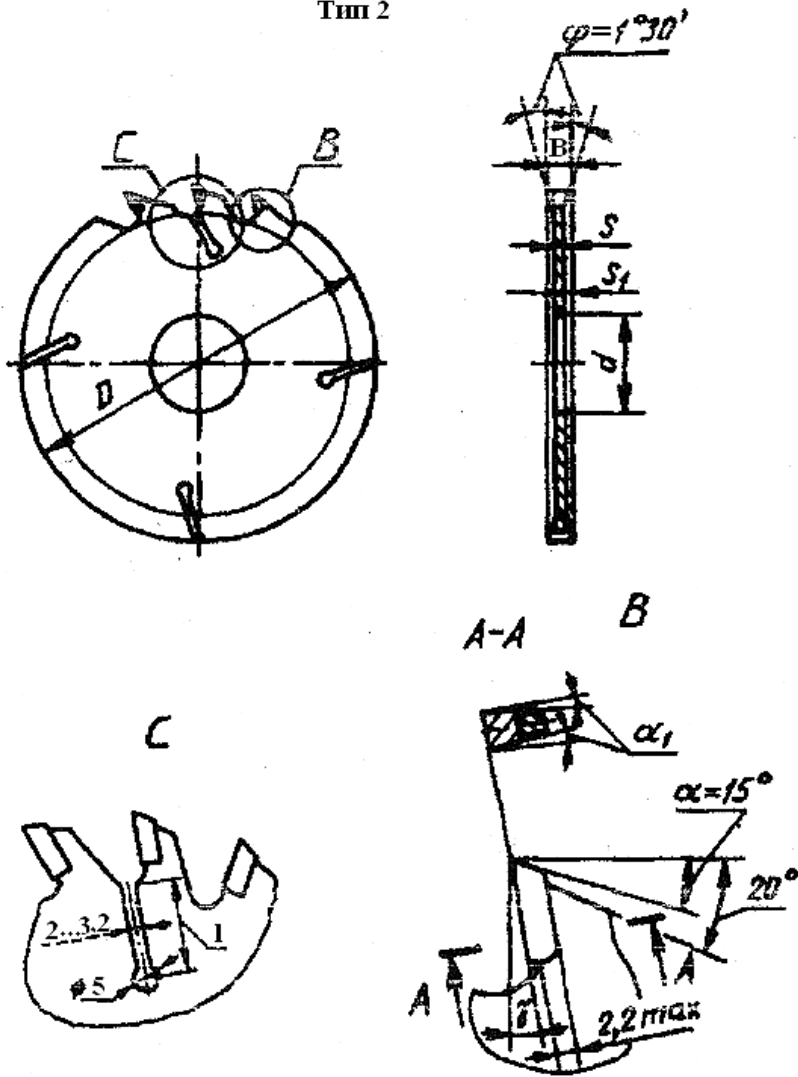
Кругла пила з пластинками з твердого сплаву
